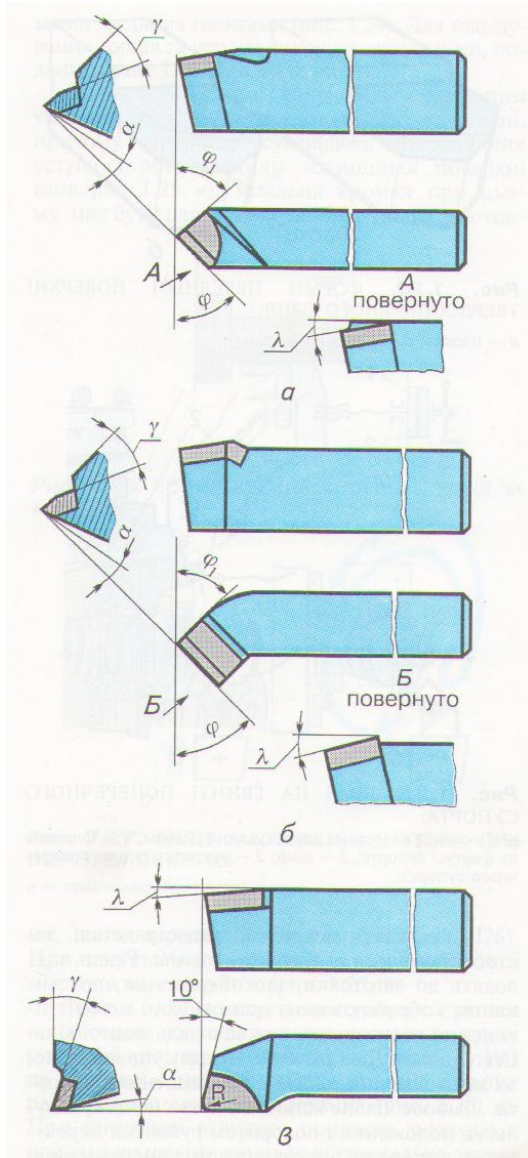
Різи для обробки зовнішніх поверхонь:
